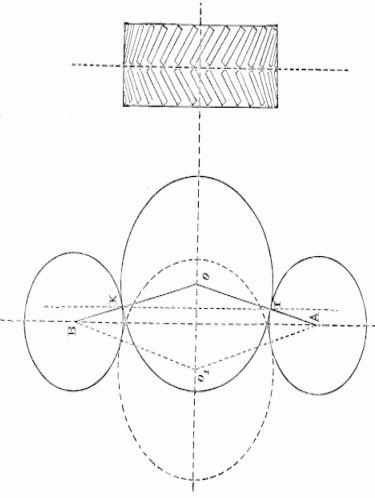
Changement de marche pour machine à 3 cylindres horizontaux.
